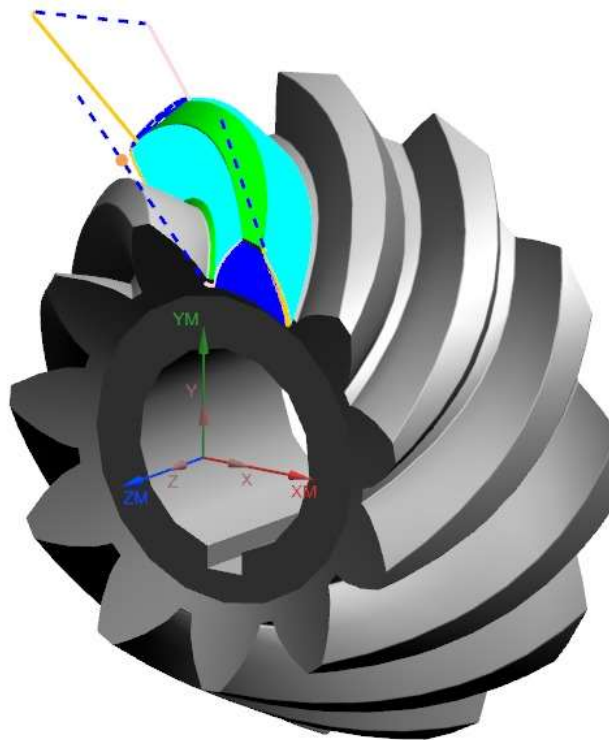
Resultado estrategia, operación “Impeller blade finish”
